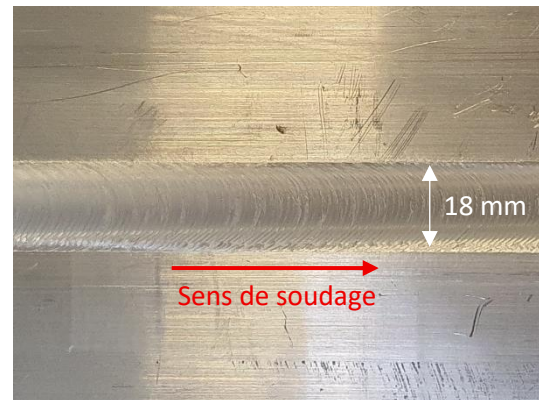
Photographie de la surface inférieure de la soudure T6 (outil B, 800 tr/min, 900 mm/min)
